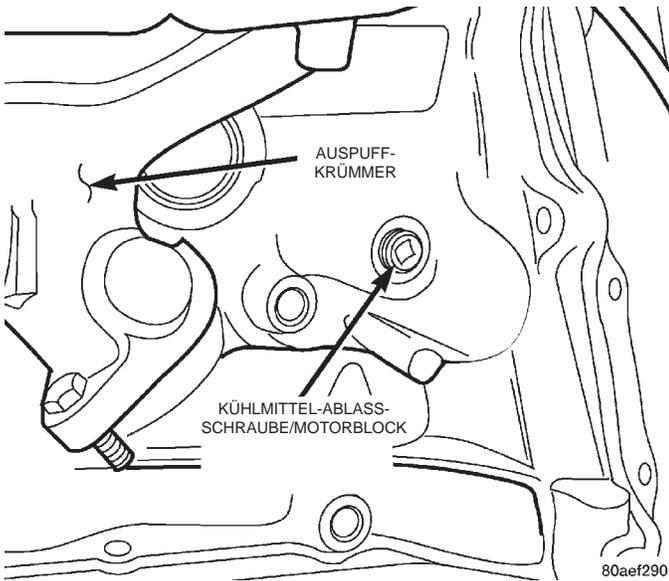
Ablassen des Kühlmittels aus dem Motorblock—2.5L-/4.0L-Motoren
